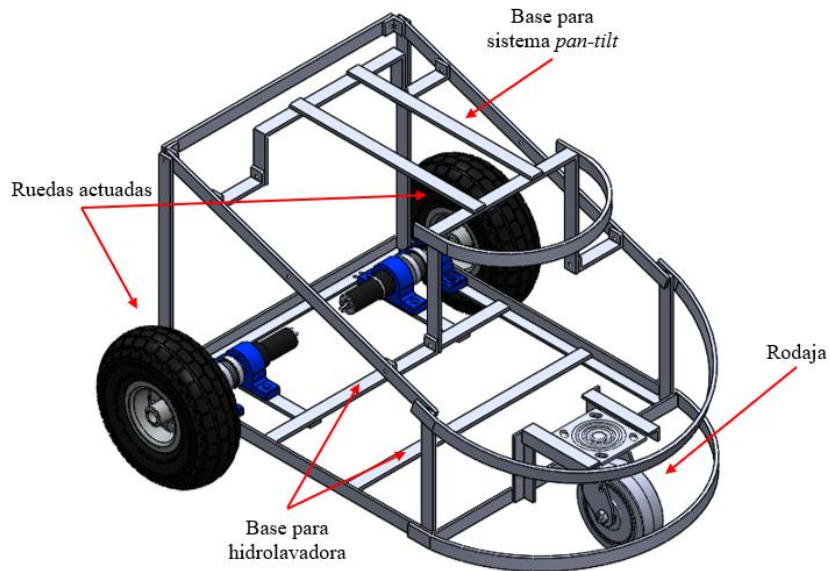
Vista isométrica del diseño CAD de la base móvil.
